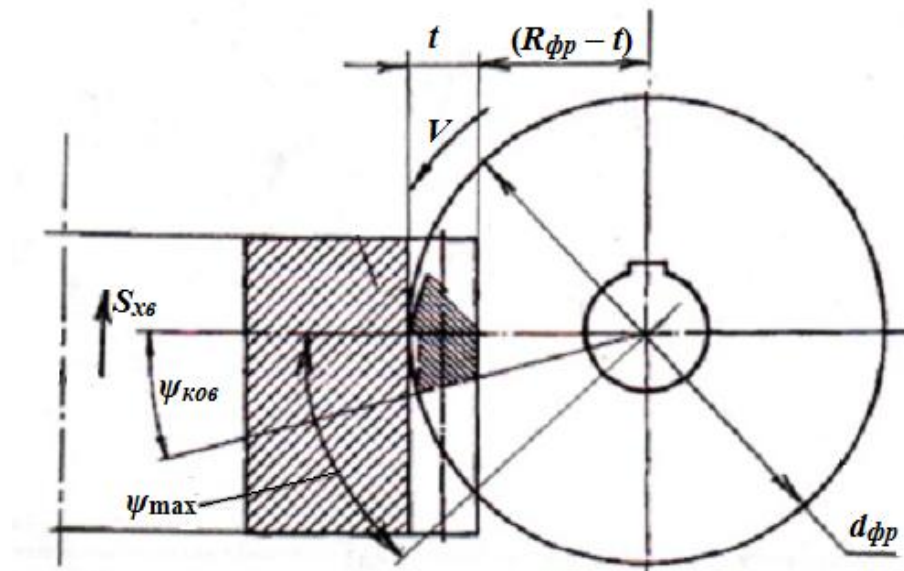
Схема розрахунку параметрів обробки при зубофрезерування відновлених зубчастих коліс
